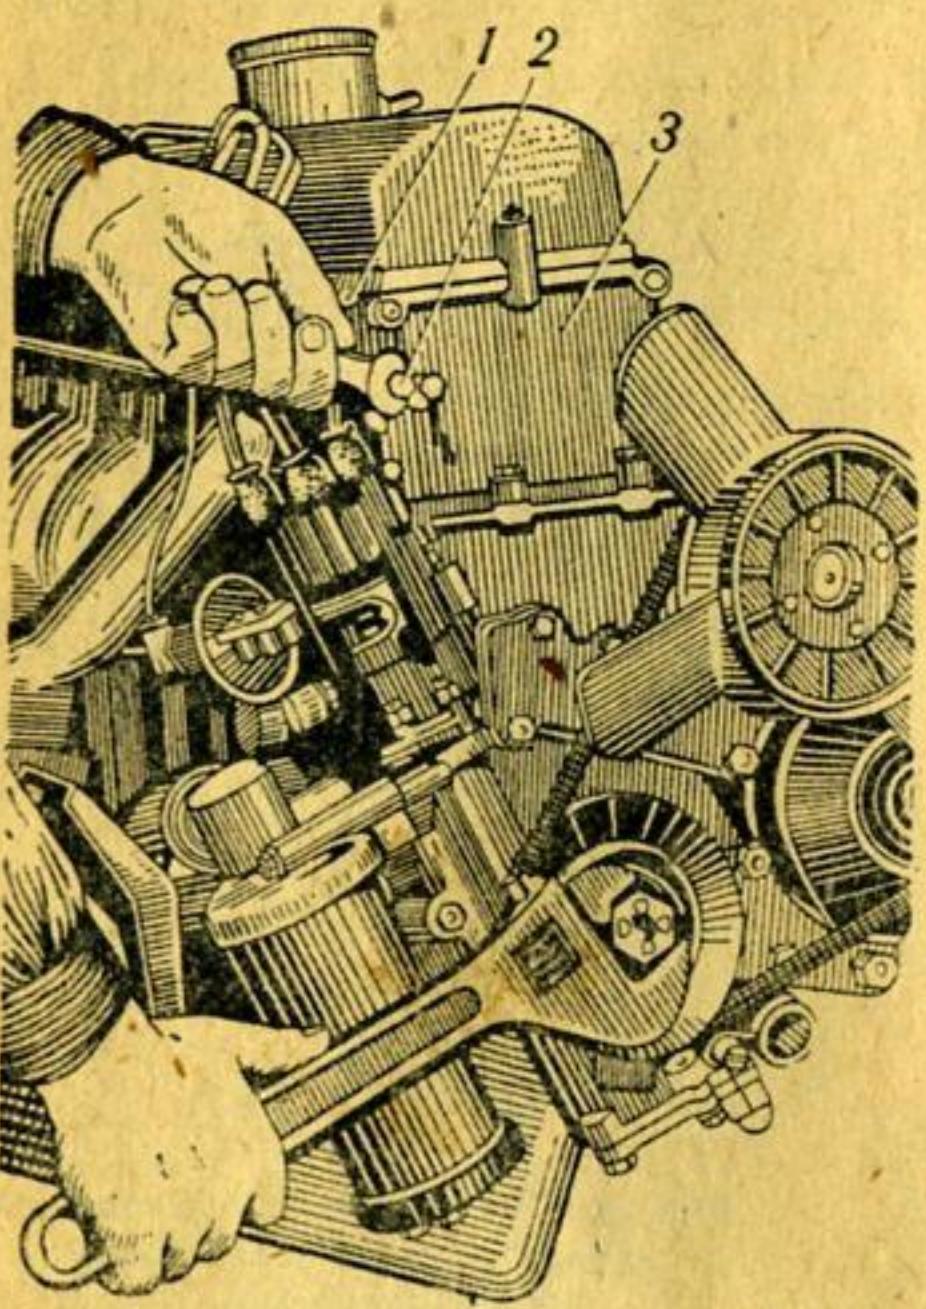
Регулировка натяжения цепи привода газораспределения:
